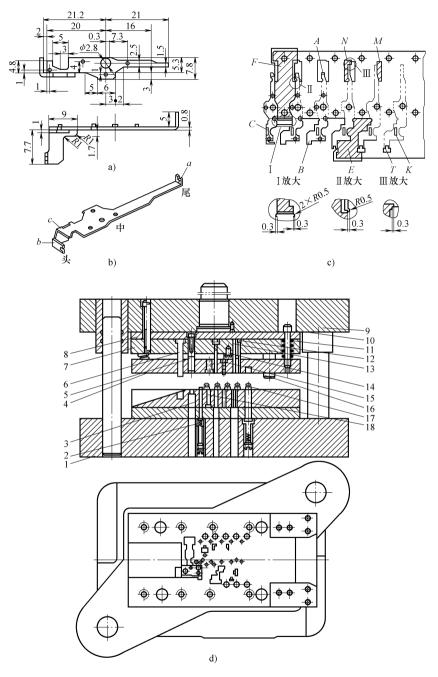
录音机机芯自停连杆多工位级进模 a) 工件图 b) 立体图 c) 排样图 d) 模具结构图
